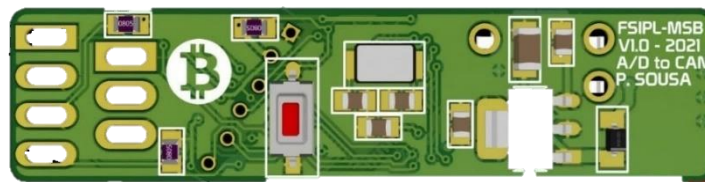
Design Final do Módulo Sensor da Posição da Caixa de Velocidades - 3D
